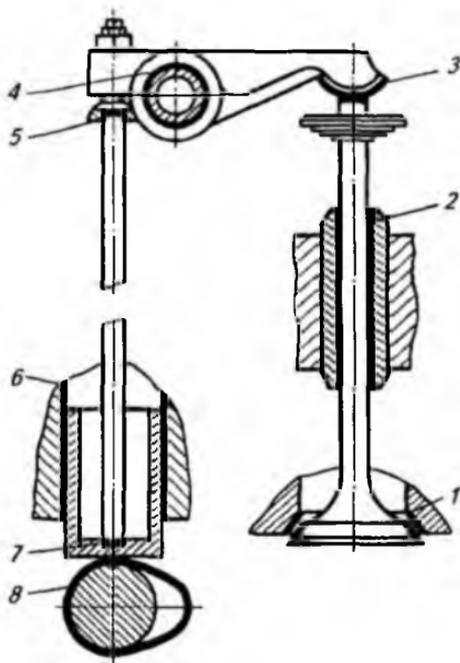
Схема изнашивающихся соединений механизма газораспределения:
